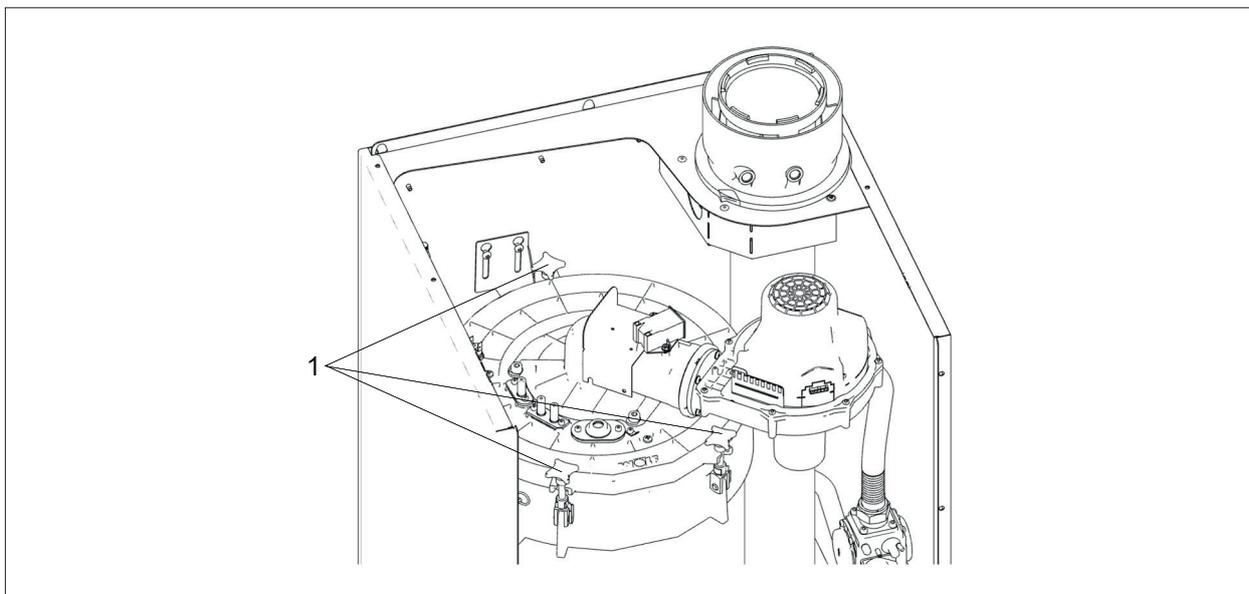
Desserrer les vis à croisillon du couvercle de la chambre de combustion
